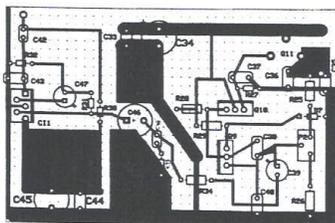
PLACA DE FIXAÇÃO IMPRESSA DO MODULADOR - LADO DOS COMPONENTES
